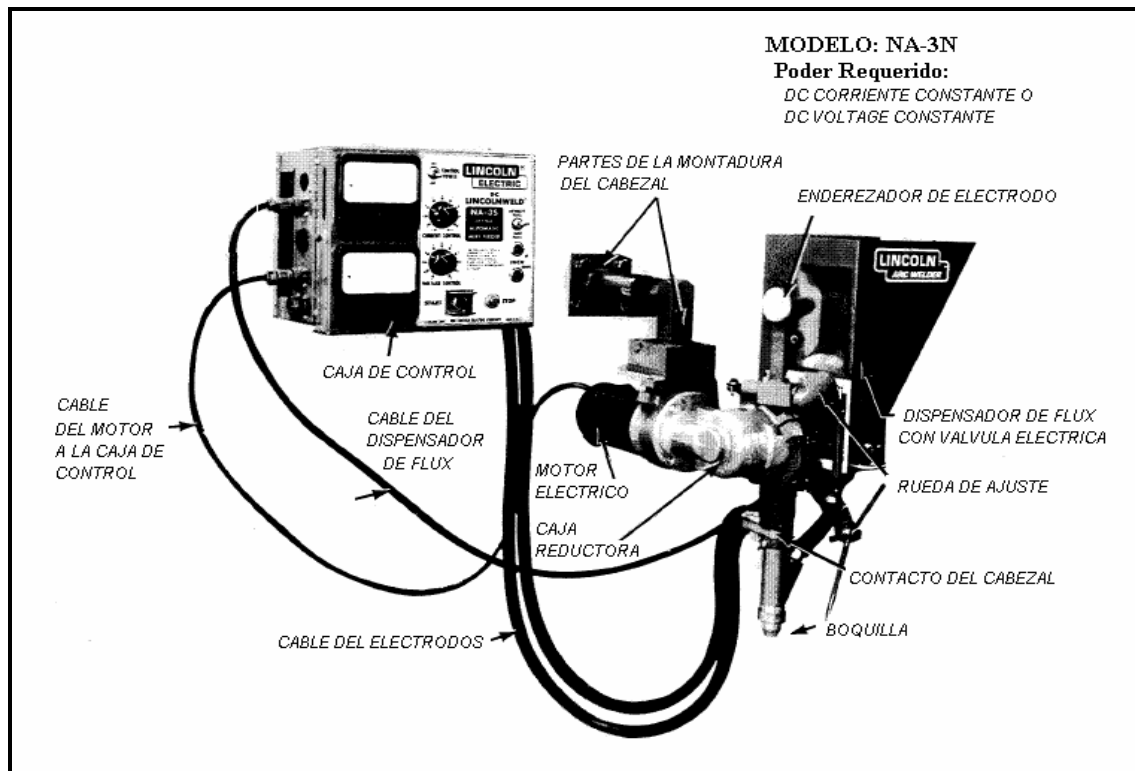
Partes del cabezal de soldadura Utilizado por la maquina formadora de tubería
